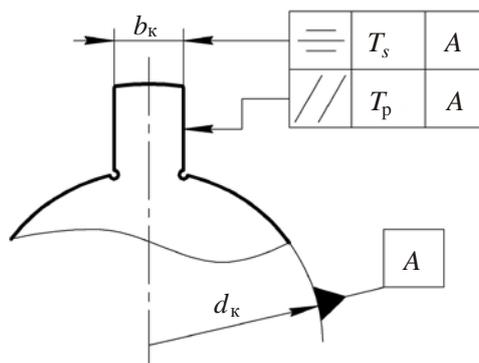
Требования к расположению боковых сторон зуба калибра-пробки при центрировании по d
